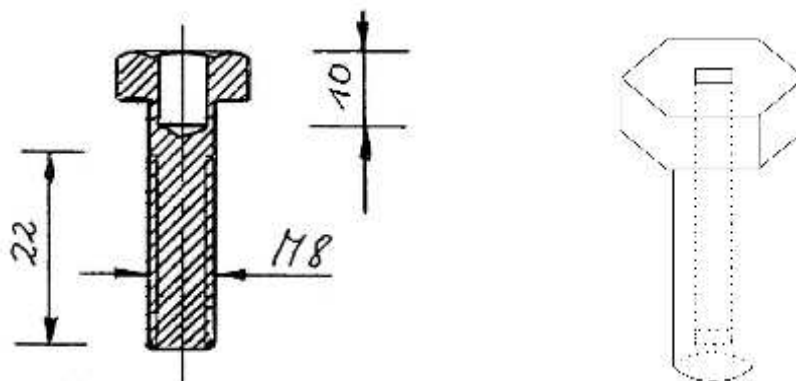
Querschnitt einer am Kopf aufgebohrten M8-Schraube (links). Skizze einer Schraube mit Profilbohrung zum Einsatz von Imbusschlüsseln zum Festziehen der Schraube (rechts).
